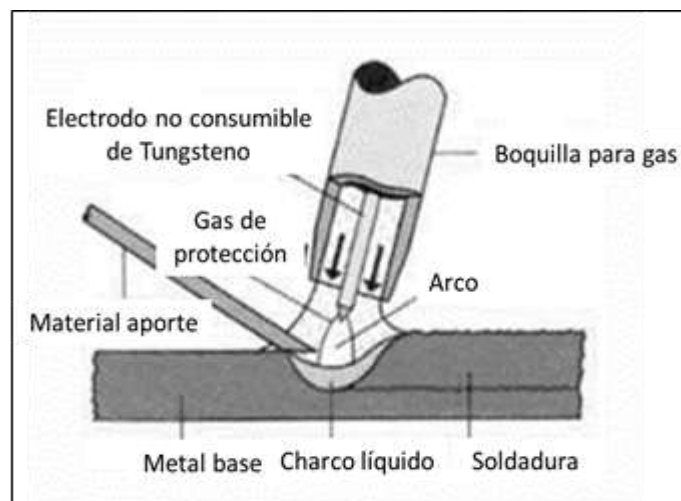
1 Esquema de soldadura GTAW (2)
